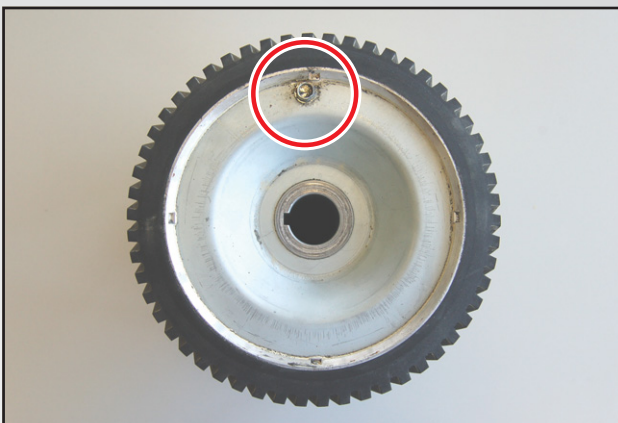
Schleifwalzenkörper mit altem Wuchtgewicht
